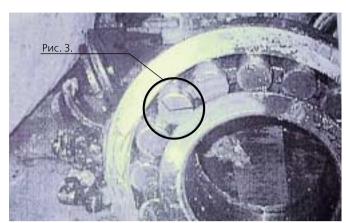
Ролик качения центрального подшипника расколот – точка измерения t2
